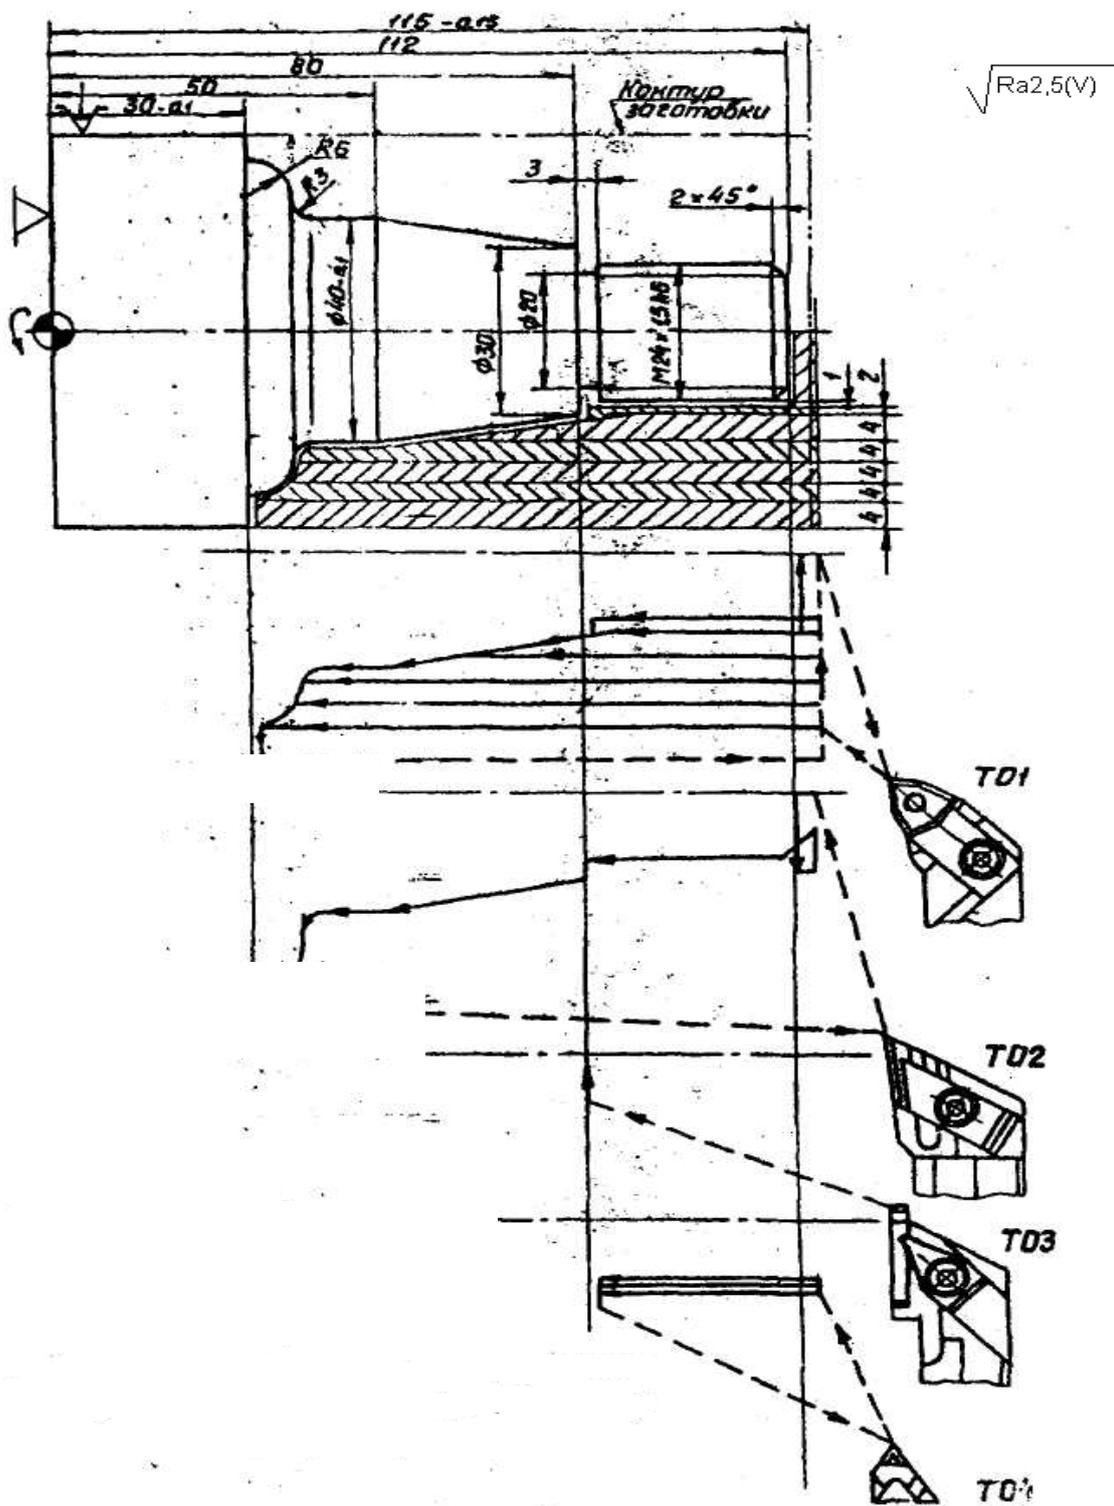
Схема наладки токарного станка с ЧПУ 16K20Ф3С5
